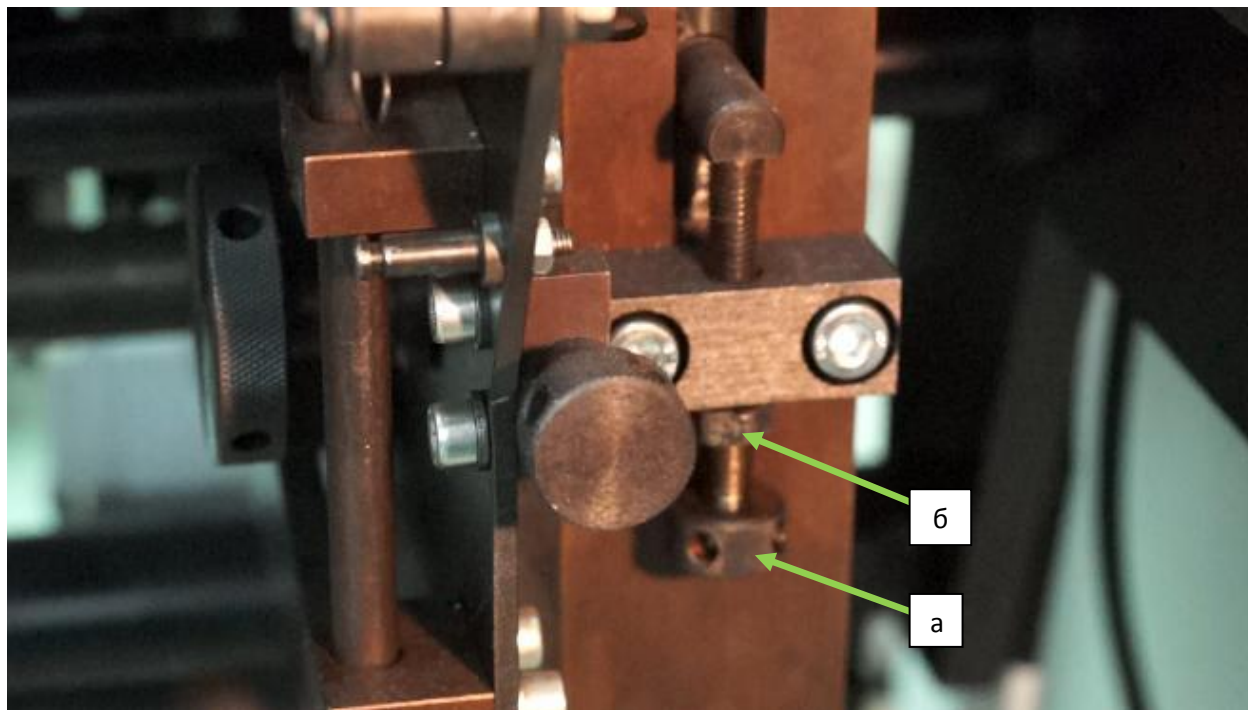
Упорный винт (а) и контргайка (б) механизма регулировки исходного положения
